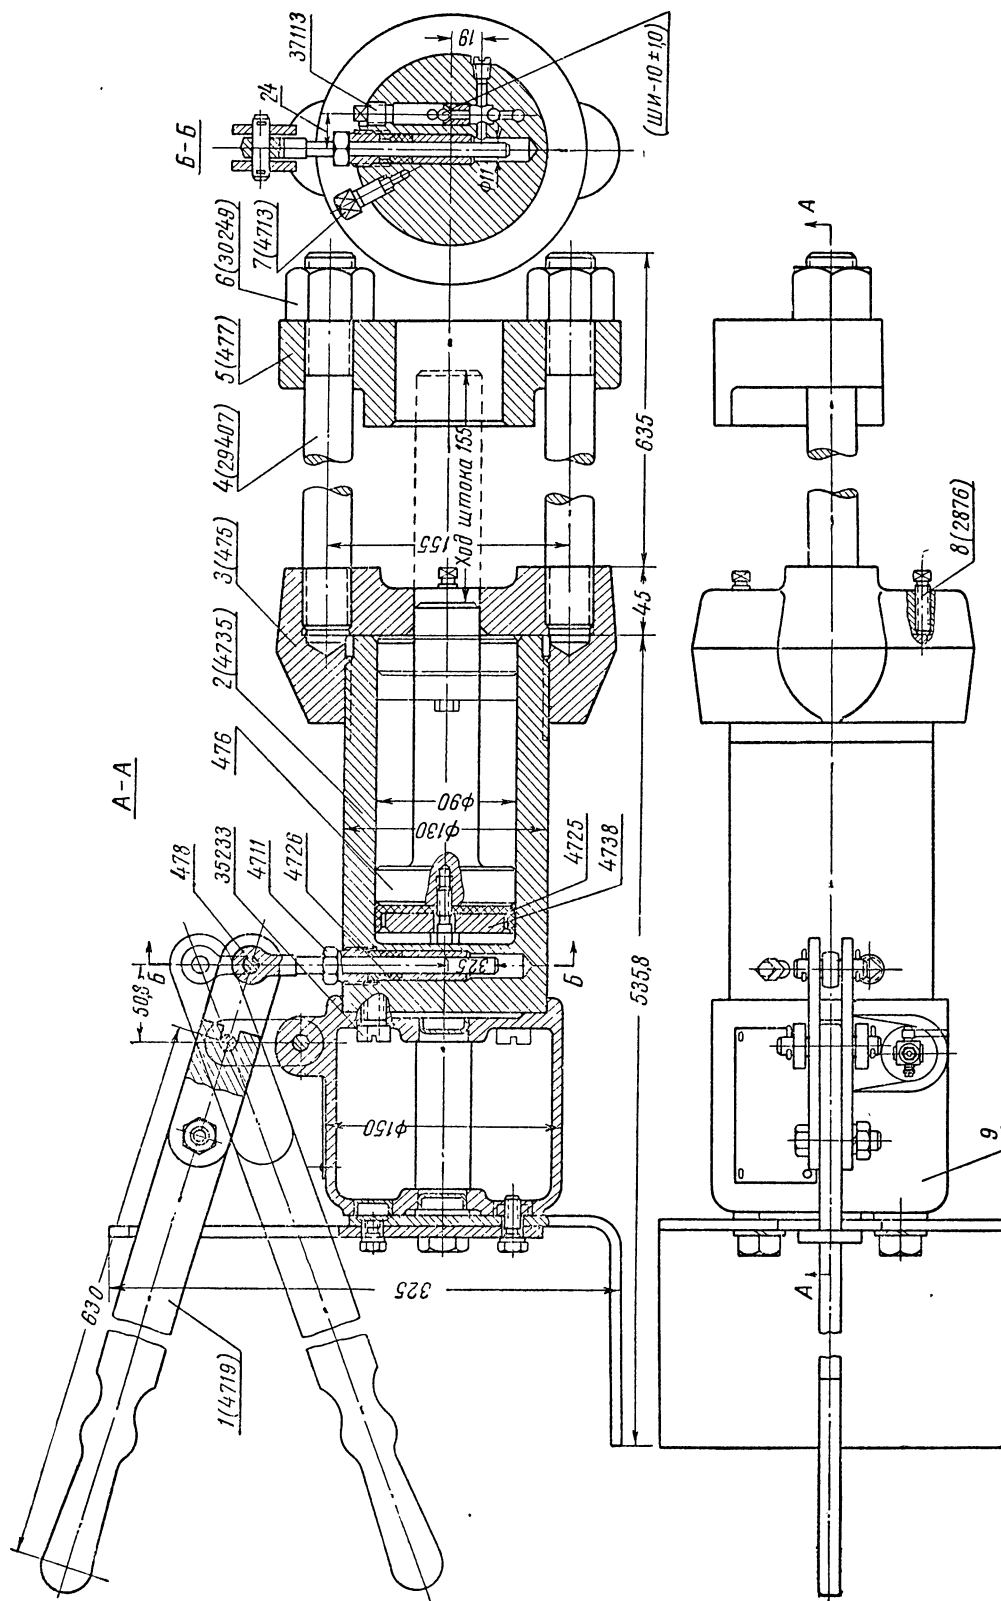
Ручной гидравлический пресс для разборки и сборки гусеницы:
